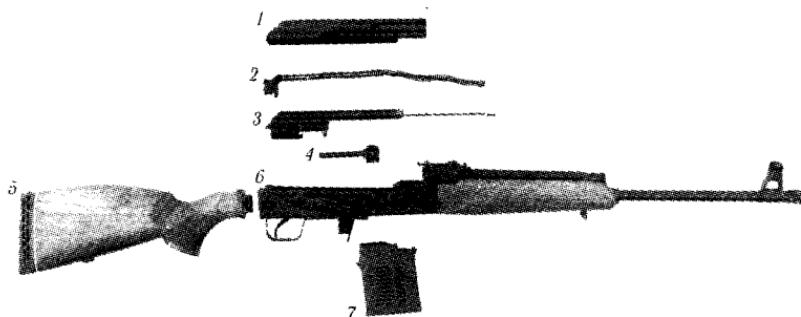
Частичная разборка карабина «Сайга-308»: 1 — крышка коробки, 2 — возвратная пружина с направляющей и защелкой, 3 — затворная рама в сборе со штоком, 4 — затвор, 5 — быстросъемный приклад, 6 — ствольная коробка, ствол, газовая камера в сборе, 7 — магазин.
